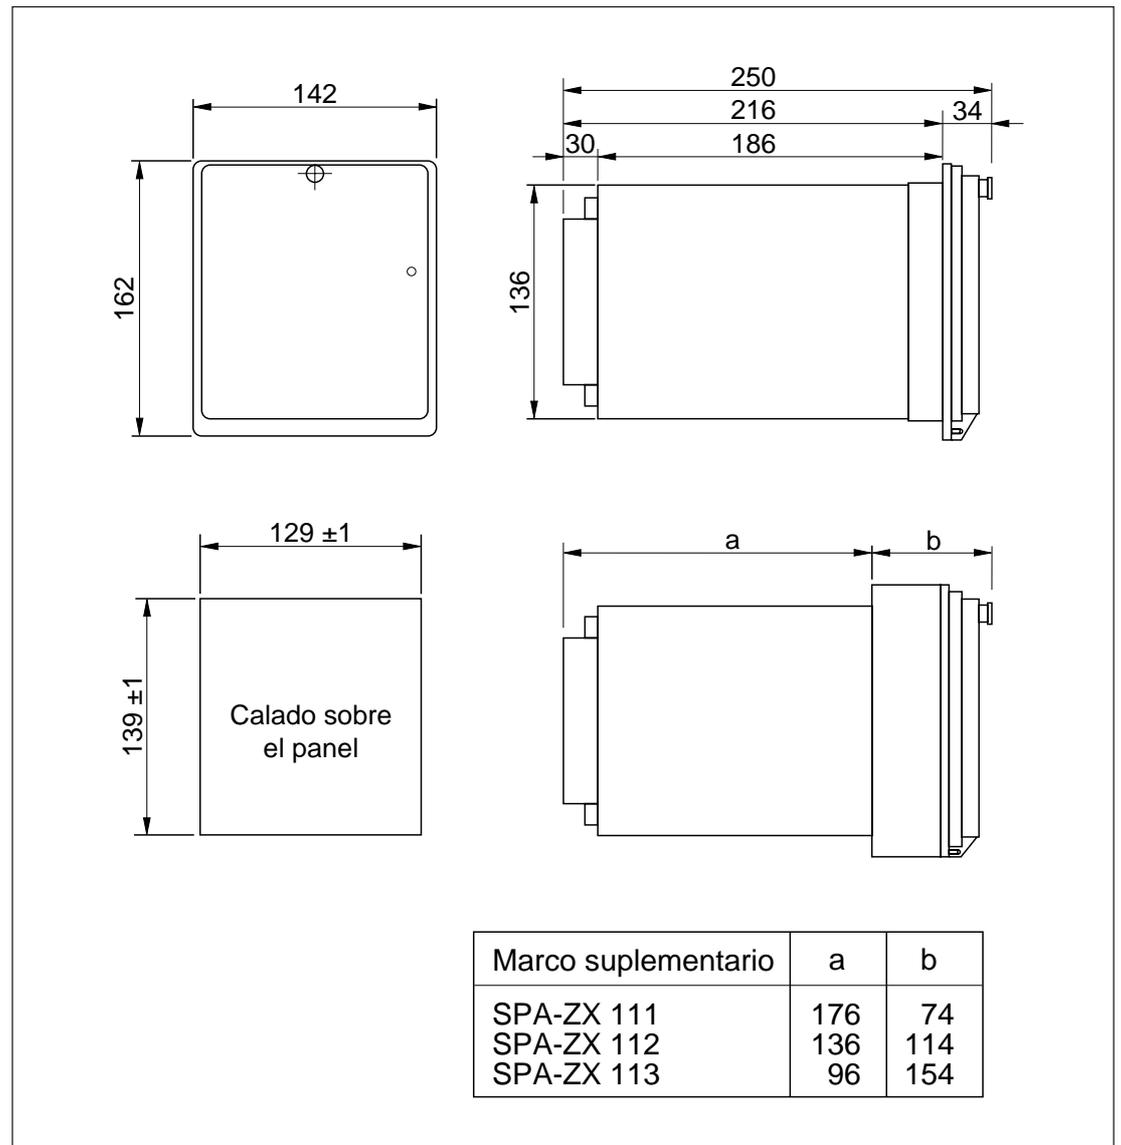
Dimensiones del relé de falla a tierra SPAJ 110 C
